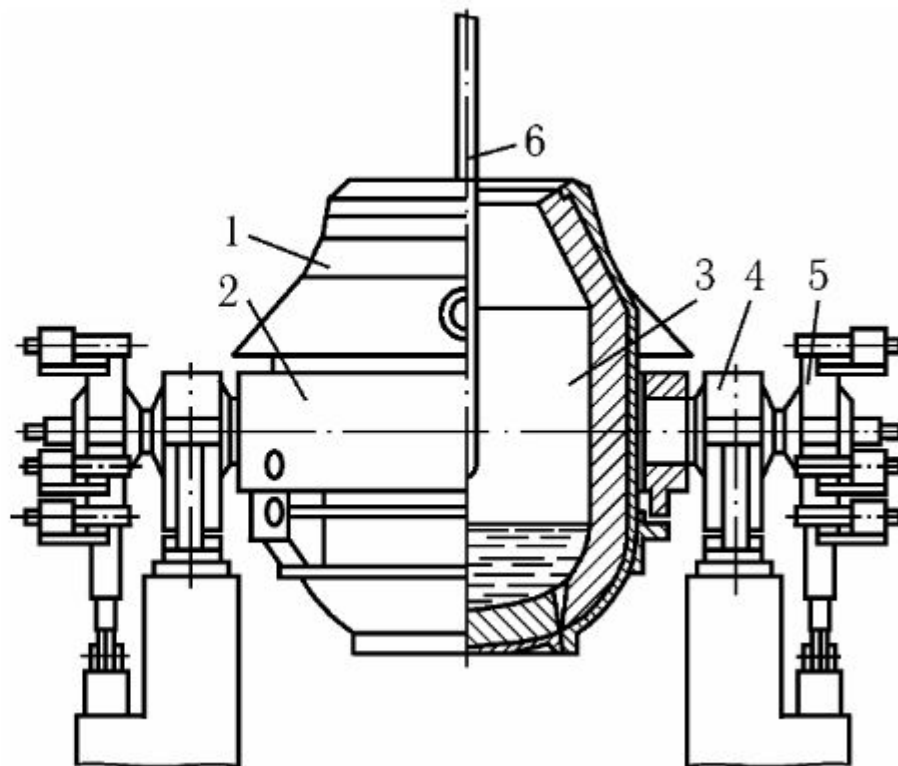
Кислородный конвертер: 1 – корпус; 2 – опорное кольцо; 3 – рабочее пространство; 4 – опорный узел; 5 – механизм поворота; 6 – кислородная фурма
